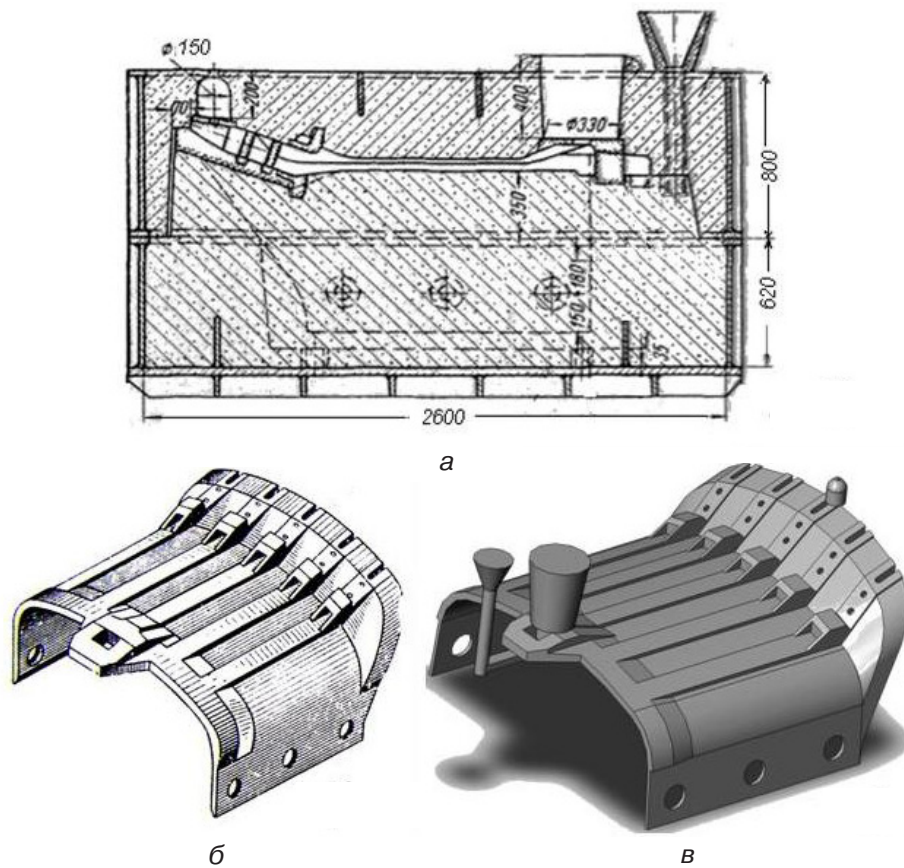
Передняя стенка ковша экскаватора: схема литейной формы (а); общий вид (б); готовая 3D модель с элементами литниковопитающей системы (в)
